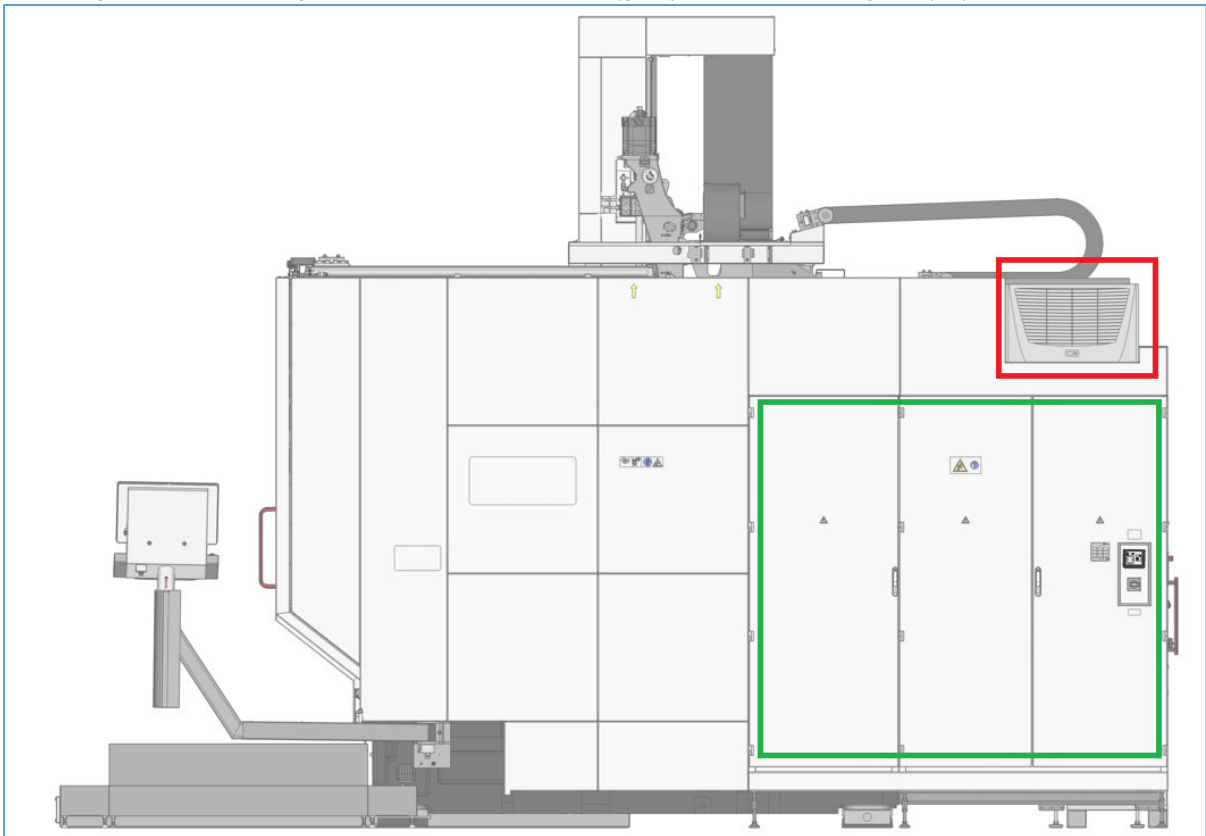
CNC-Werkzeugmaschine mit Schaltschrank (grün) und einem Klimagerät (rot) im Dachanbau
